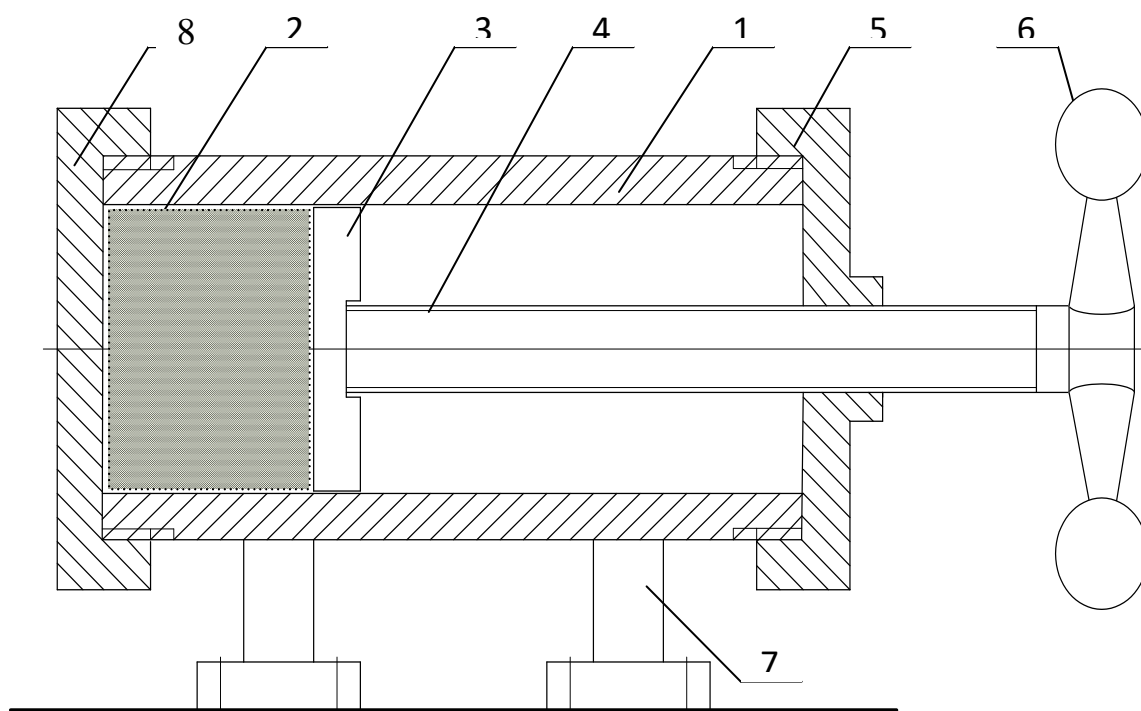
Схема установки для пелетирования: 1 – материальный цилиндр; 2 – исходная смесь для пелетирования; 3 – поршень; 4 – шток с винтовой нарезкой; 5 – задняя крышка; 6 – рукоятка; 7 – съемные опоры; 8 – передняя крышка
